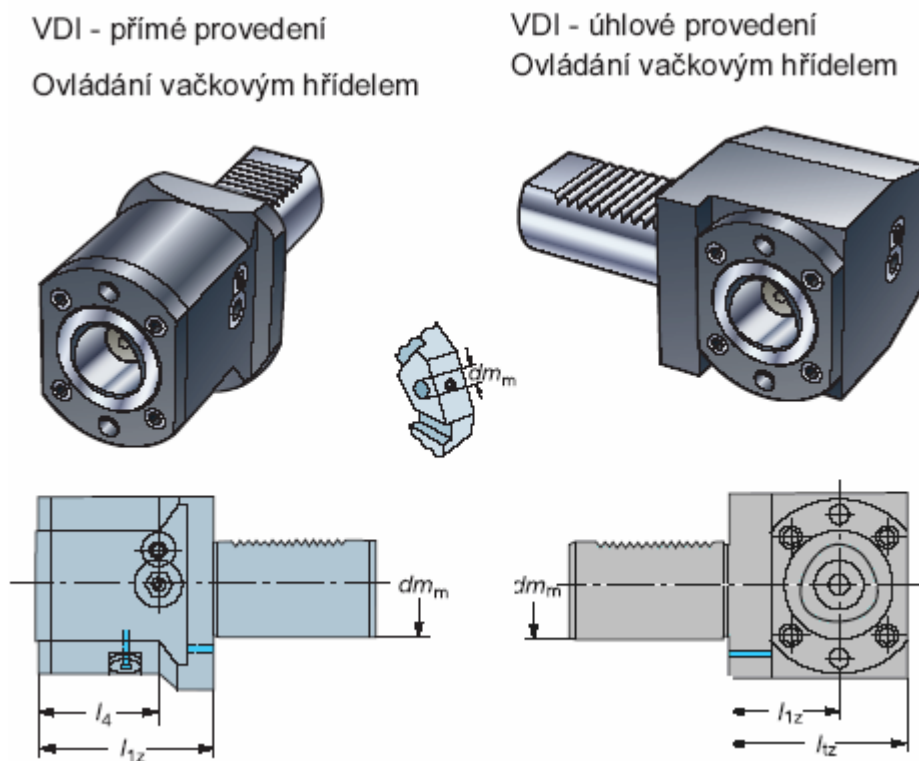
Pevné VDI držáky ²Obr. 4.27 Poháněné VDI držáky ²
